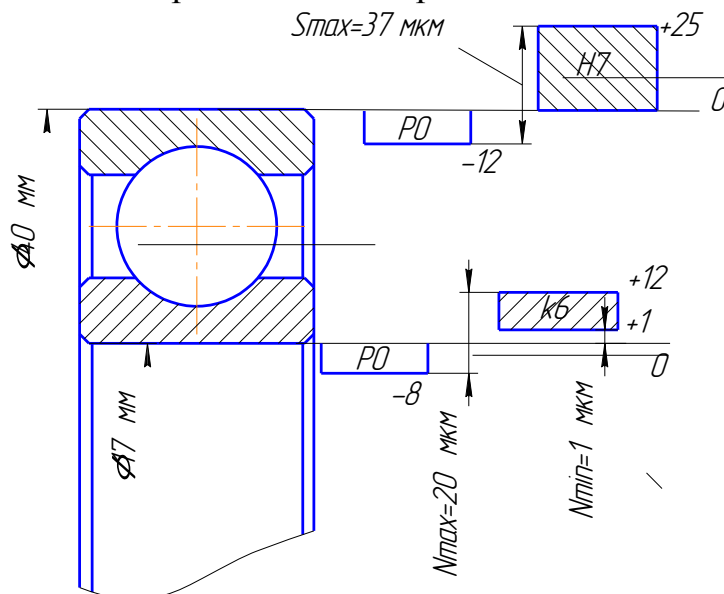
Схема расположения полей допусков на диаметры колец подшипника качения.
